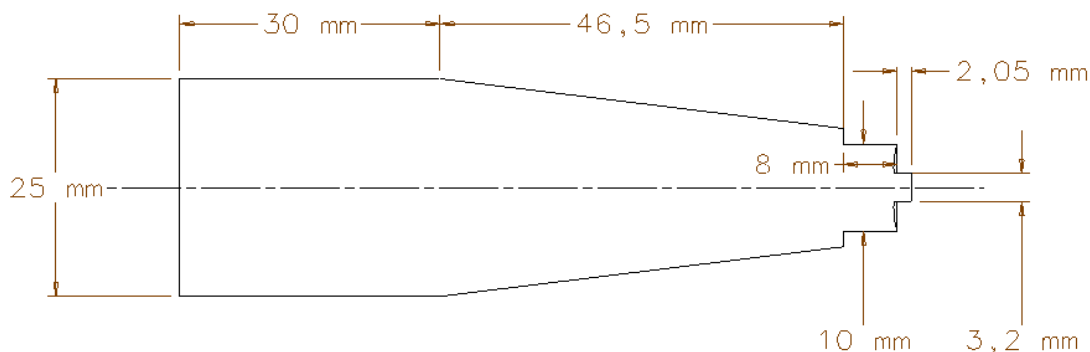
Outil utilisé pour le soudage des échantillons SFM.
